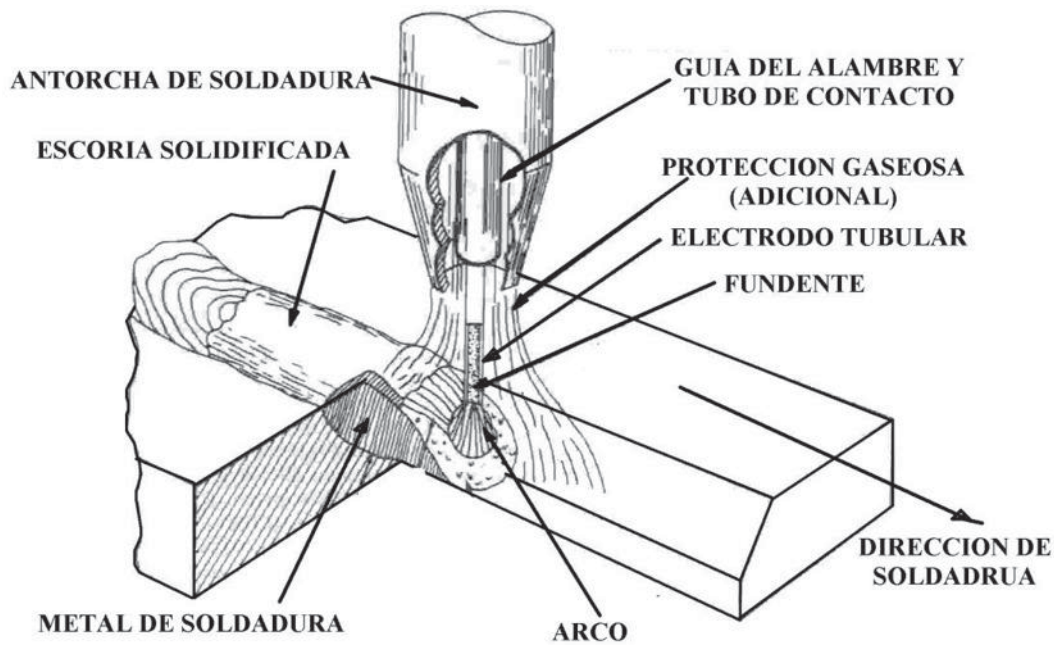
12 Esquema del proceso soldadura por arco con electrodo tubular
